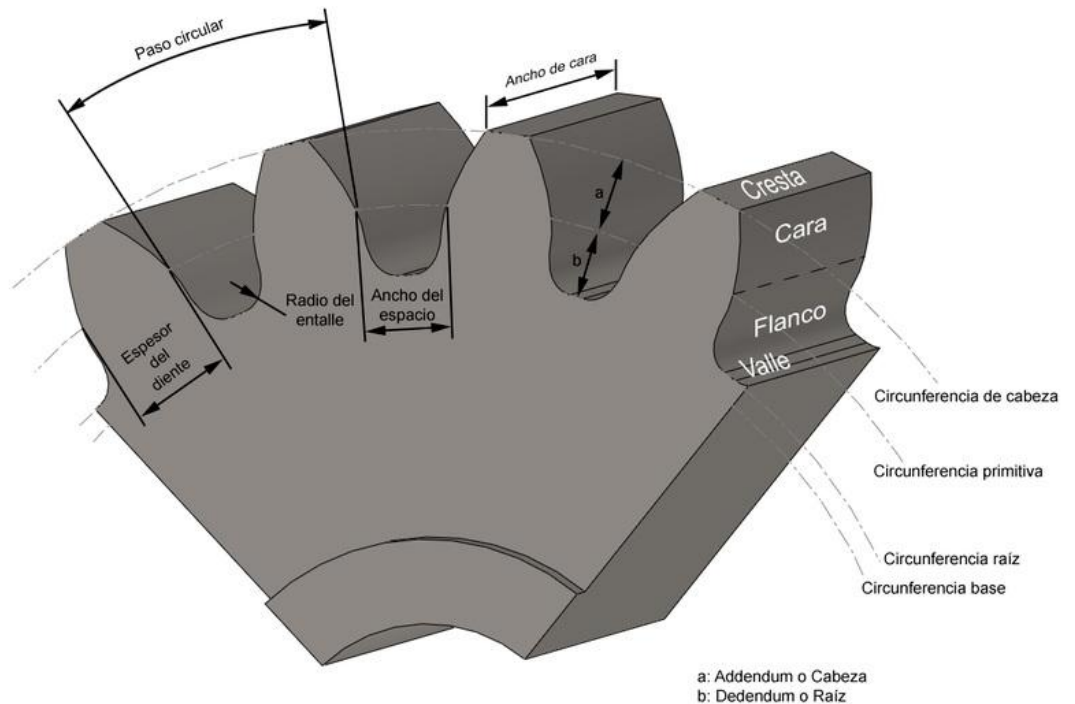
Elementos de un engranaje (diseño IZANTUX).
